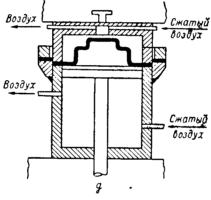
Схемы формования с использованием универсальной камеры.
